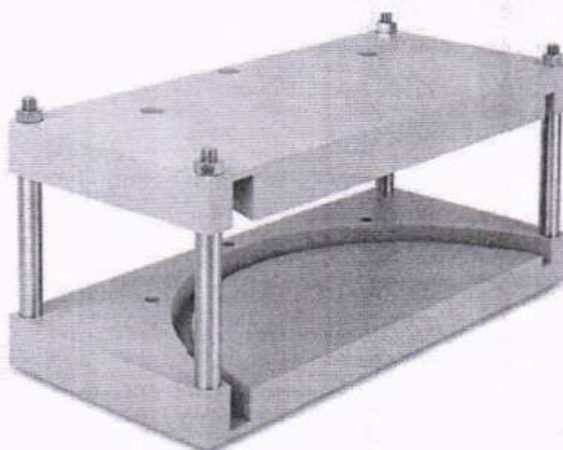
Внешний вид оснастки для поверки гибкого детектора
